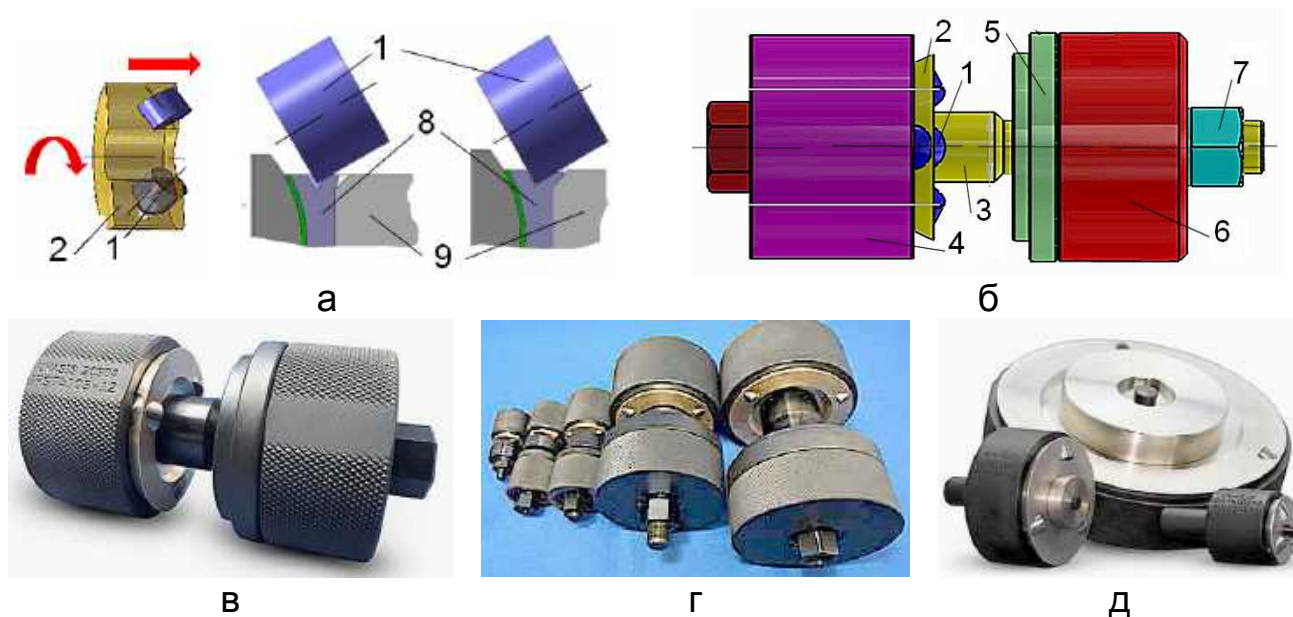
Роликове розкочування авіаційних сферичних підшипників ковзання з V-подібним пазом на зовнішньому кільці: 1 – ролик; 2 – сепаратор; 3 – штир; 4 – корпус; 5 – опора; 6 – державка; 7 – гайка; 8 – підшипник; 9 – деталь
